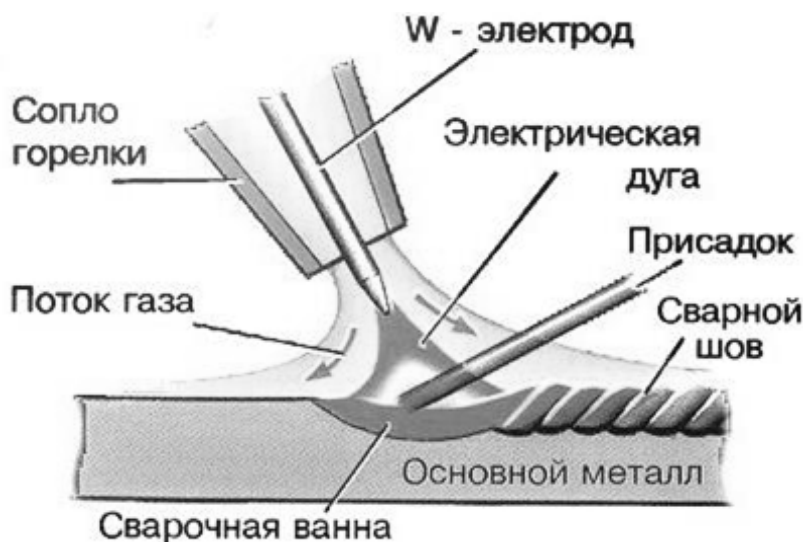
Схема сварки неплавящимся вольфрамовым электродом в защитном газе
